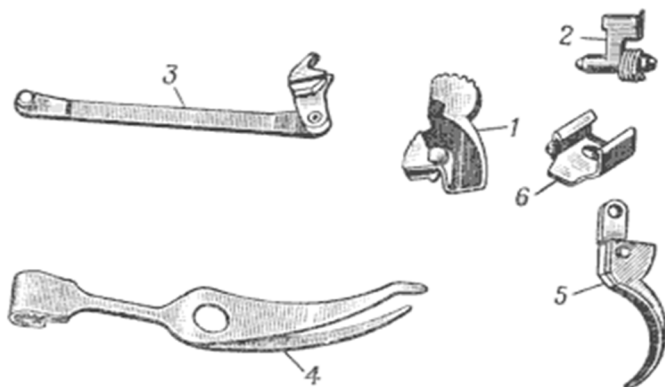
Части ударно-спускового механизма: 1 – курок; 2 – шептало с пружиной; 3 – спусковая тяга с рычагом взвода; 4 – боевая пружина; 5 – спусковой крючок; 6 – задвижка боевой пружины
